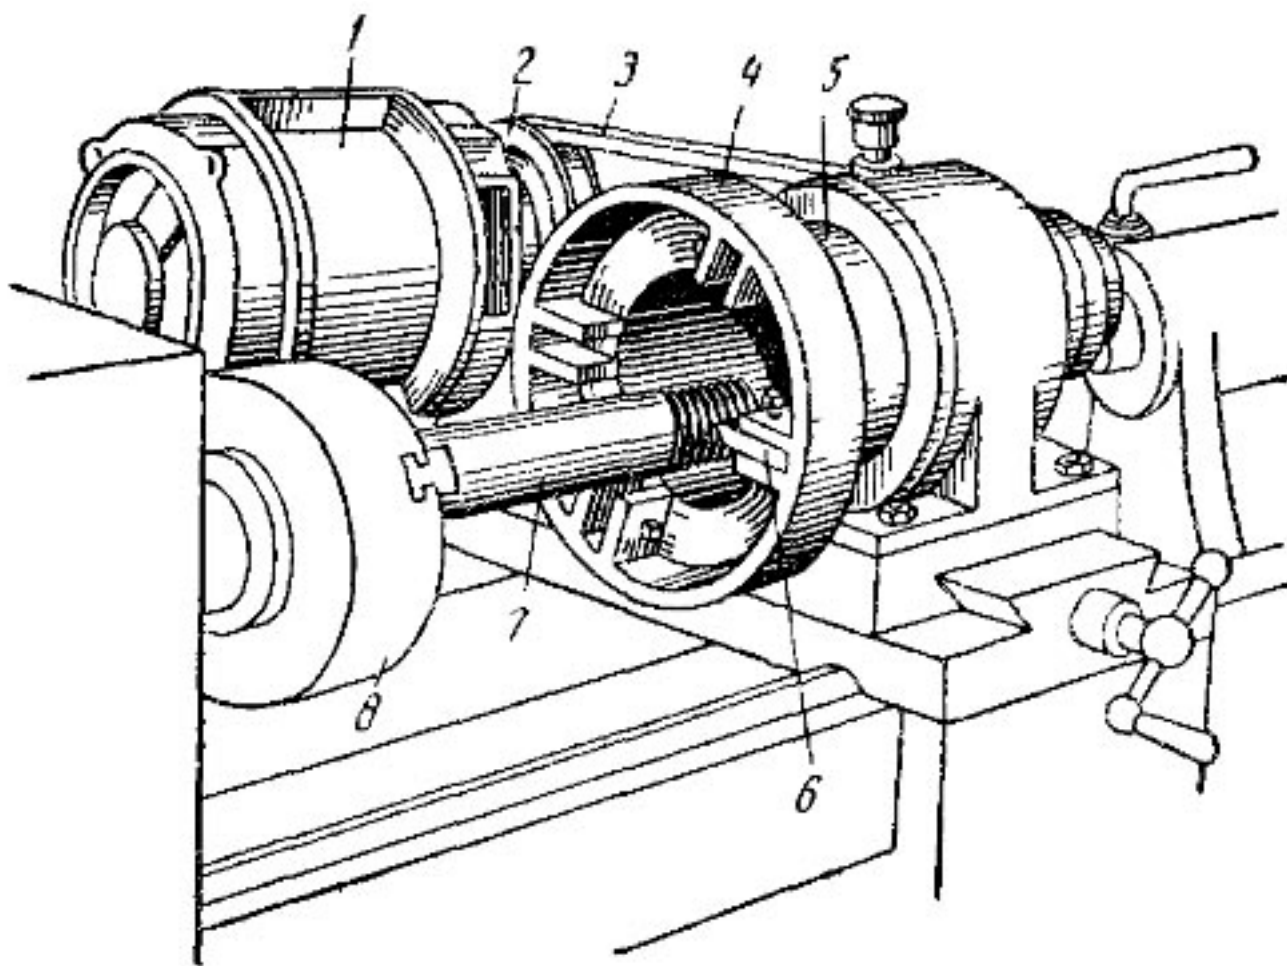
Приспособление для нарезания резьбы вращающимся резцом
